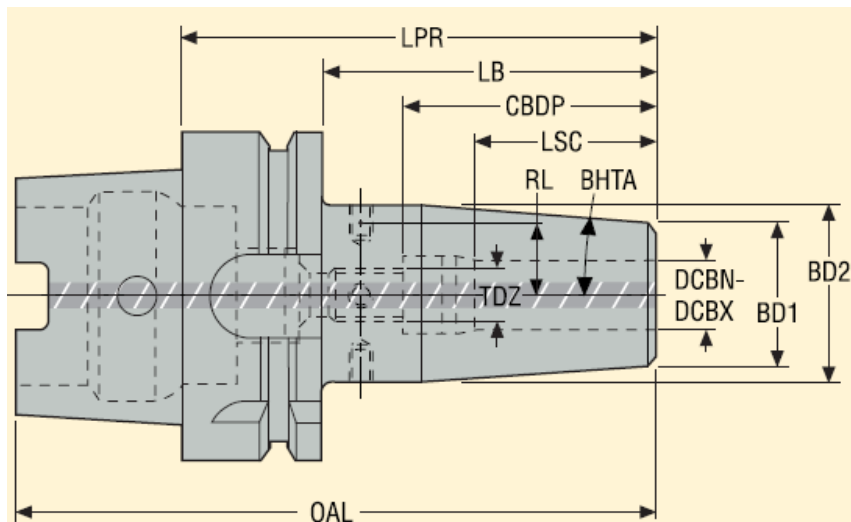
Термооправка для закрепления дисковой фрезы
